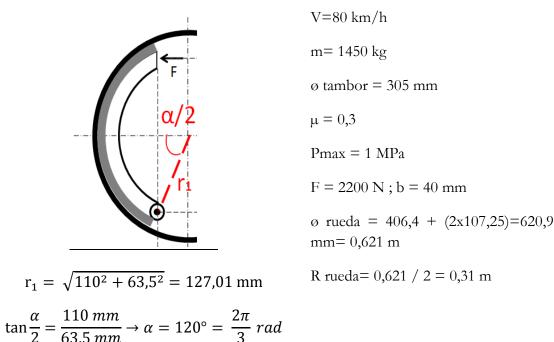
Dimensiones de la zapata del freno de tambor y dimensiones de la rueda.
